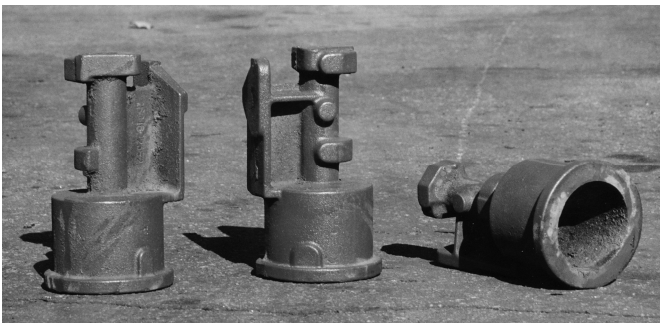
Отливка «Корпус цилиндра выключения сцепления» для грузового автомобиля КрАЗ
